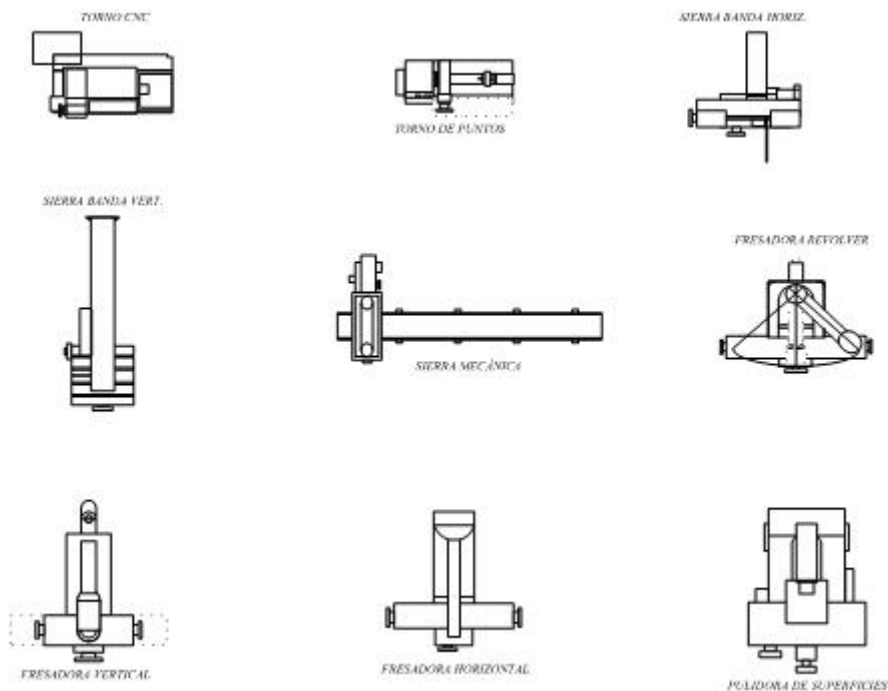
Muestras de figuras para realizar una distribución en planta
